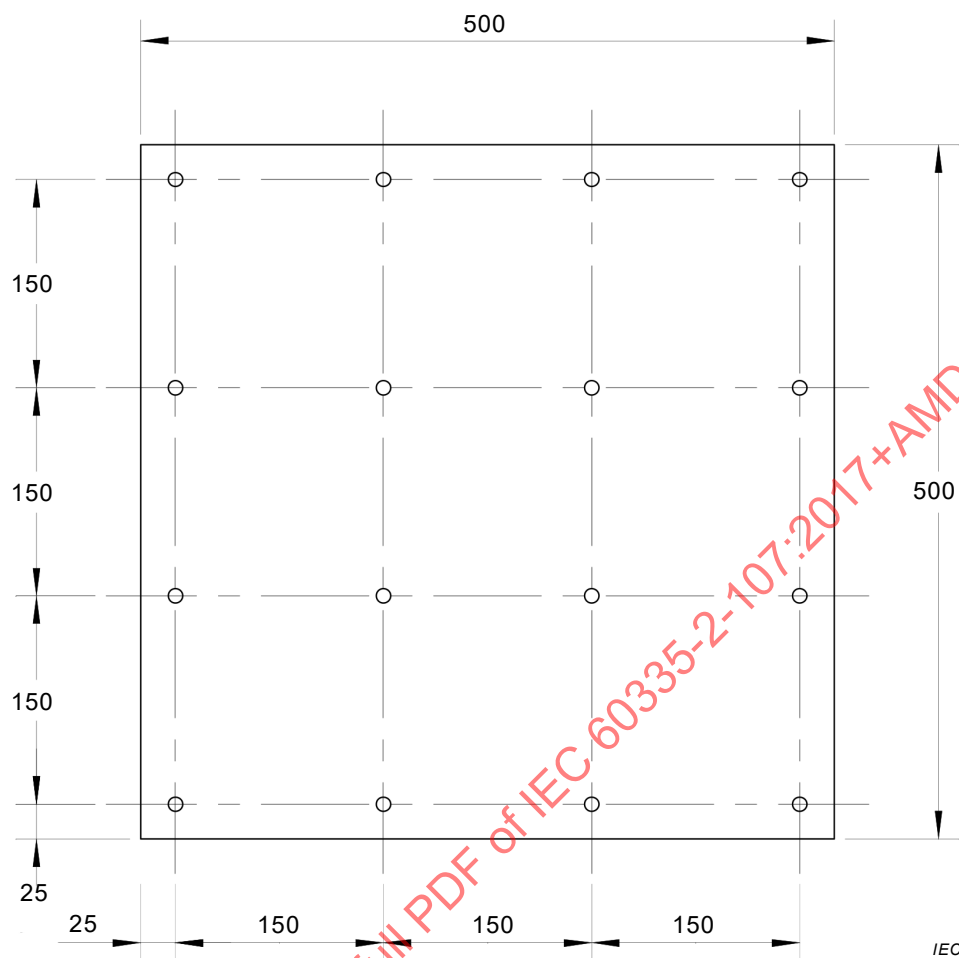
Plan de clouage du support de l'enceinte d'essai
